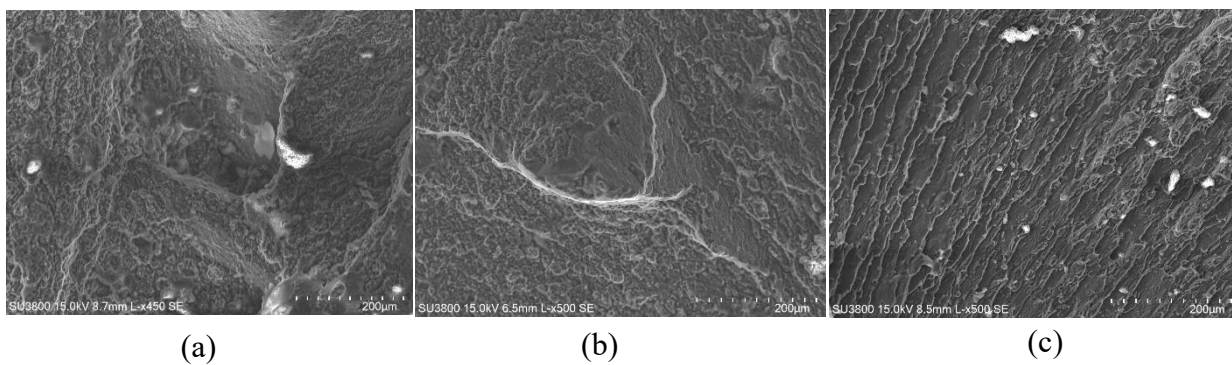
Fractografias das soldaduras S-1500-90-7,1 (a), S-870-90-7,1 (b) e S-500-90-7,1 (c).
